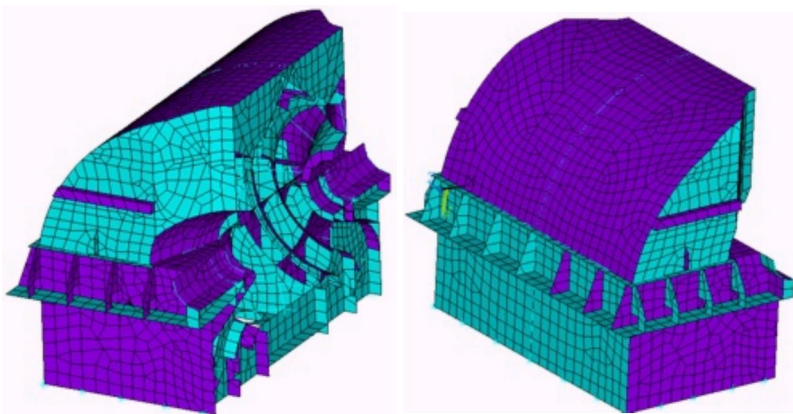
Конечно-элементная модель симметричной половины корпуса ЦНД турбины К-500 в сборе
